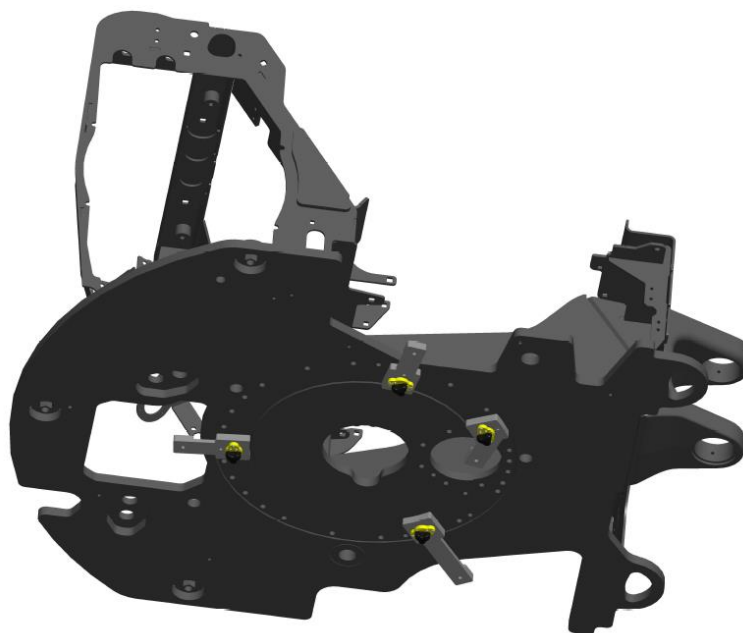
Varianta 4- Rozmery prímerného prípravku A
